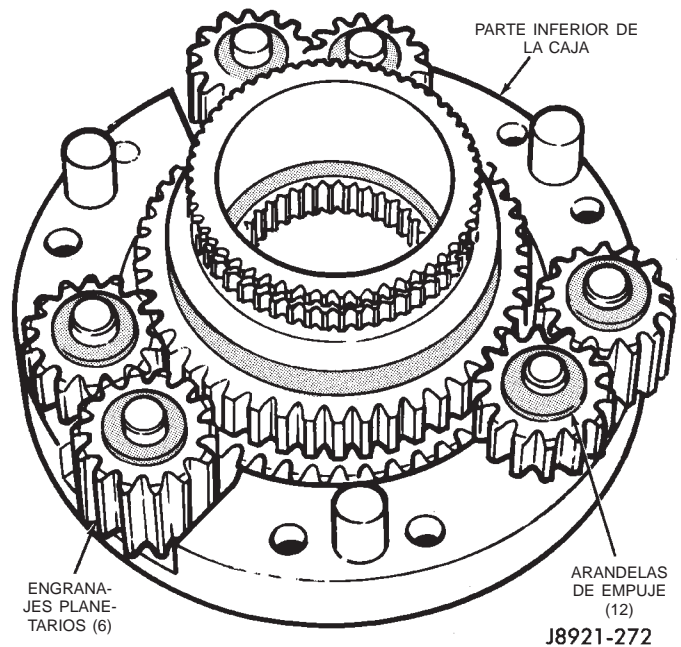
Desmontaje de engranajes planetarios y arandelas de empuje
